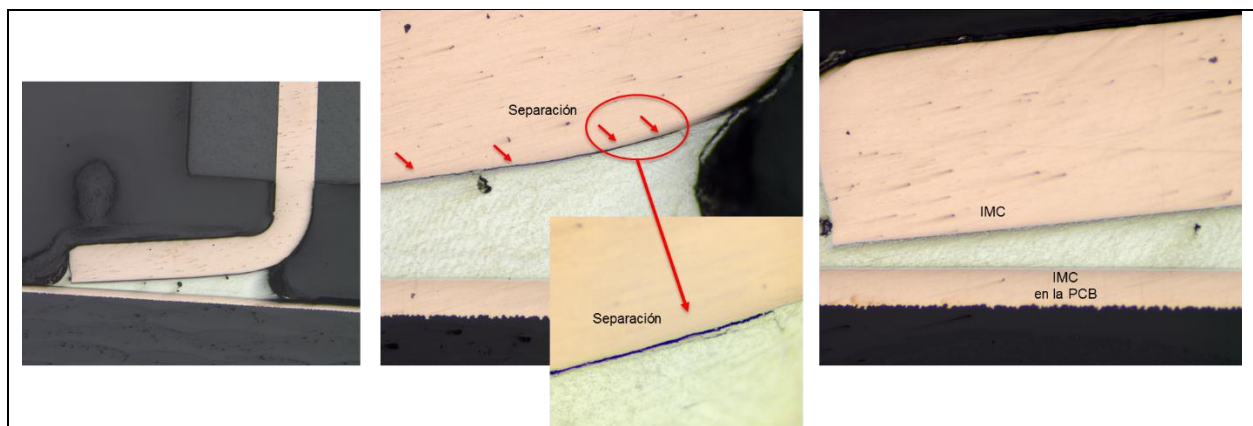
Corte seccional del LED montado en la tarjeta que muestra la separación
